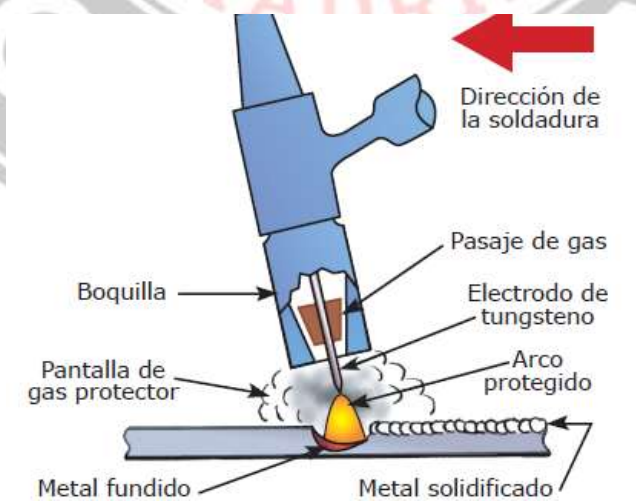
Esquema de un soplete para soldadura TIG
